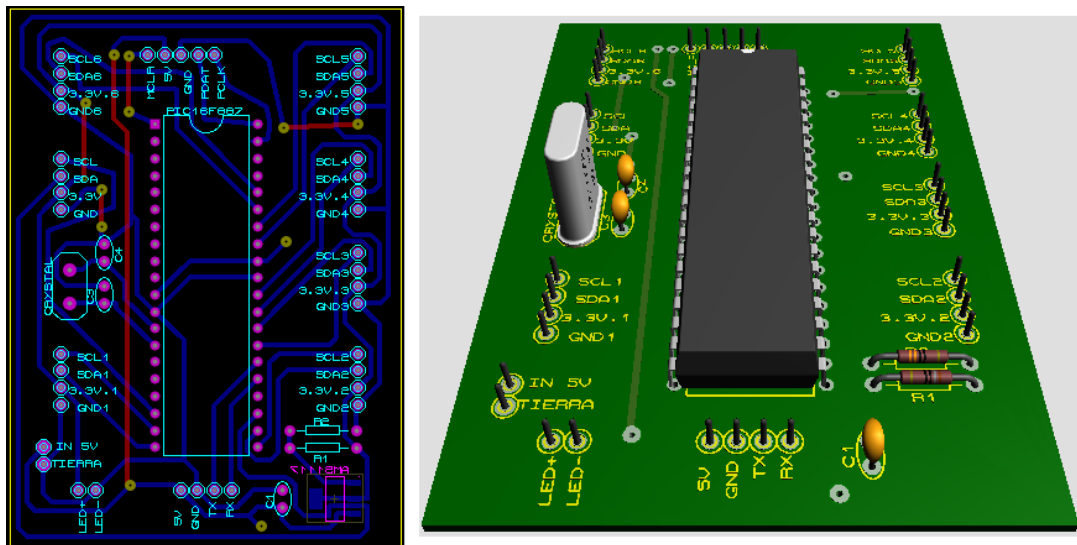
Diseño del PCB del primer prototipo en Proteus ARES.
